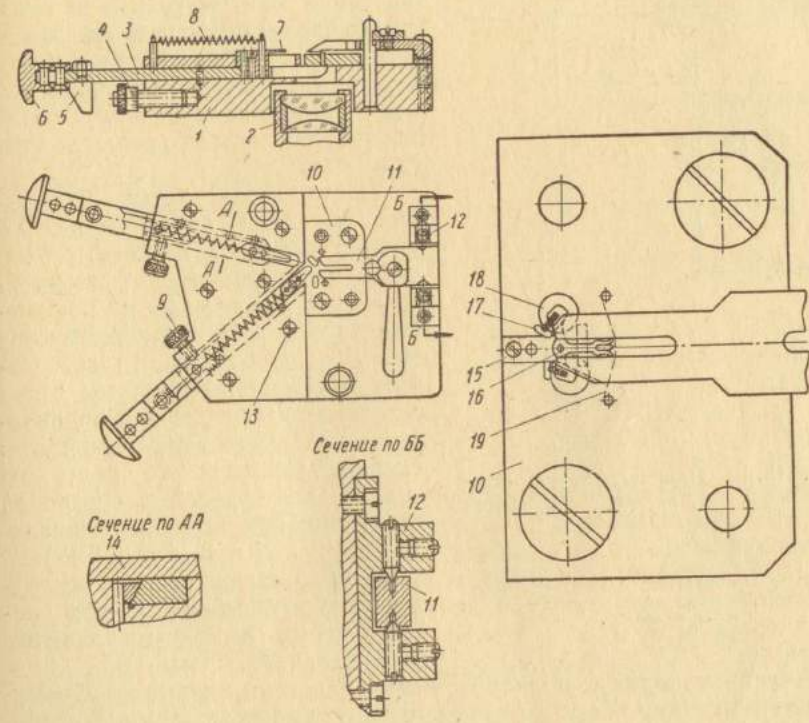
17. Общий вид агрегата сборки анкерной вилки:
